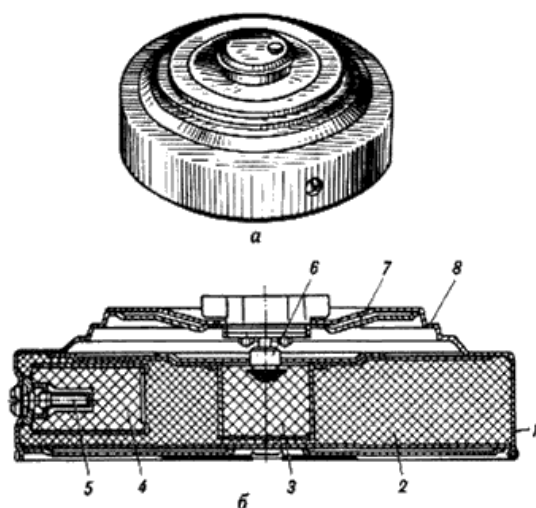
Противотанковая мина ТМ-57: *а* – общий вид; *б* – разрез; 1 – корпус; 2 – заряд ВВ; 3 – центральный промежуточный детонатор; 4 – боковой промежуточный детонатор; 5 – запальное гнездо бокового промежуточного детонатора; 6 – взрыватель МВ-57 в боевом положении; 7 – щиток; 8 – крышка
